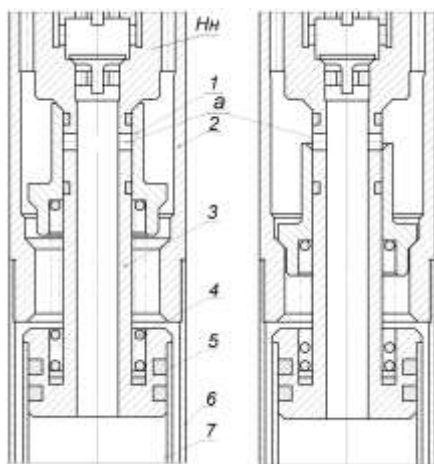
Схема НПУ с распределительным узлом в виде поршня-золотника: 1 – поршень; 2 – шток; 3 – цилиндр; 4 – пружина; 5 – регулировочные кольца; 6, 7 – наружная и внутренняя трубы колонкового набора; «Нн» - нижняя наковальня гидроударника
